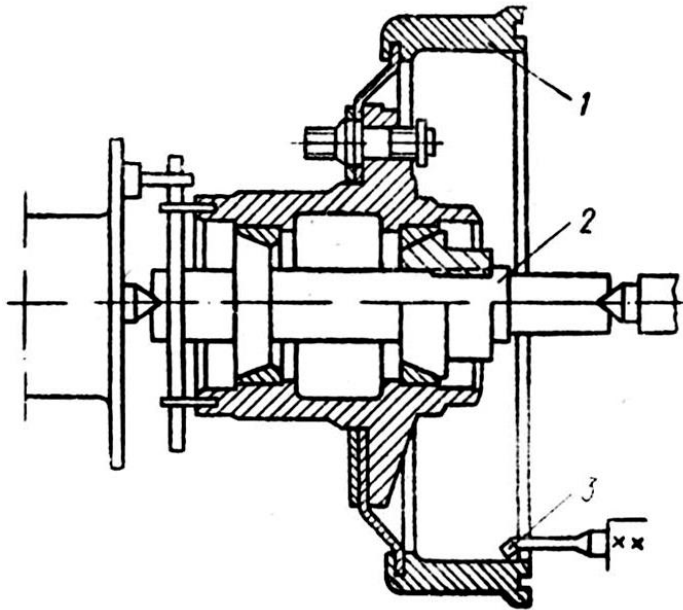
Розточування гальмового барабана на токарному верстаті:
